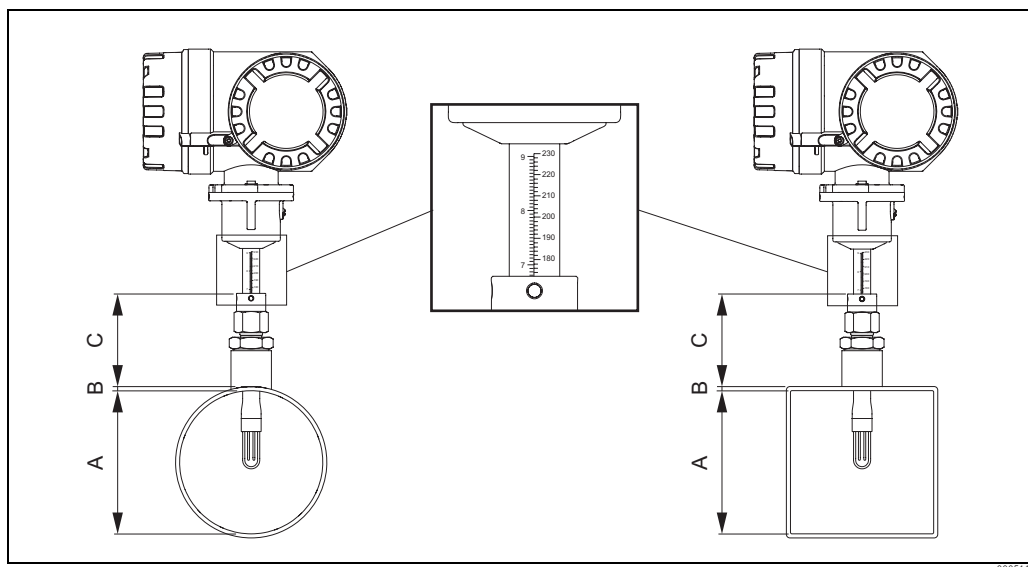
Dimensions requises pour calculer la profondeur d'immersion du capteur
